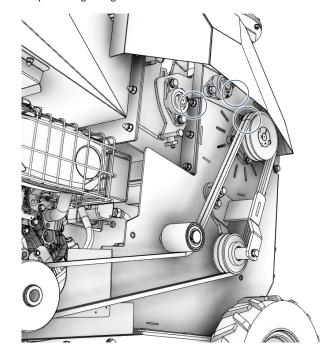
Points de graissage de la machine – vue côté gauche sans le protecteur fixe
